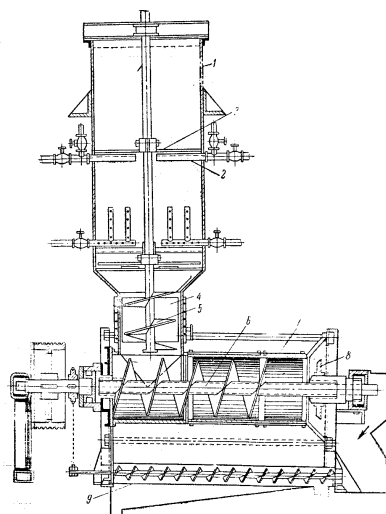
Схема форшнека КЯ: 1 – бункер; 2 – форсунки подачі пари; 3 – ножі-мішалки; 4 – патрубок; 5 – шнек-живильник; 6 – вал шнековий; 7 – циліндрзеєр; 8 – регулюючий конус; 9 – шнек для видалення олії.
